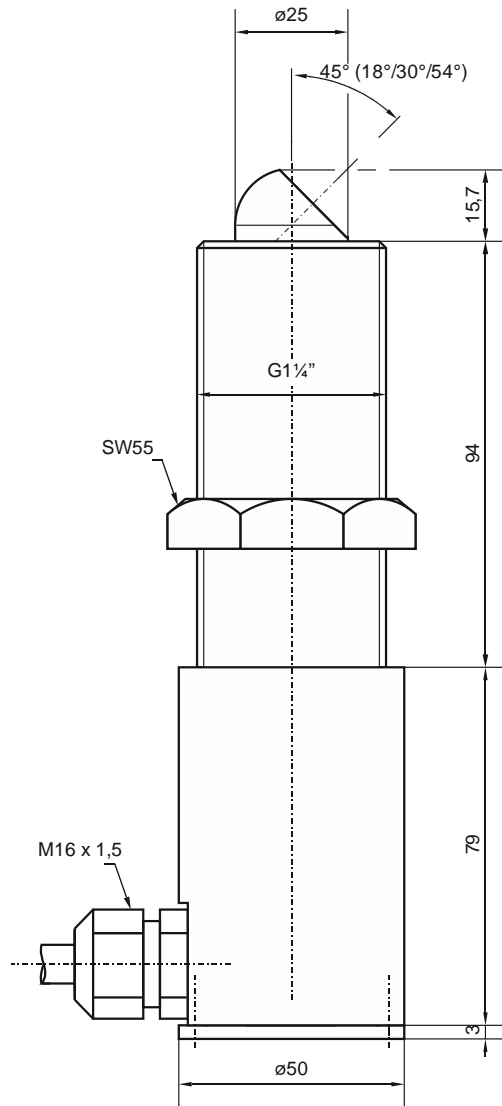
Maßzeichnung Einschraubsensor Typ NOS-V2E
